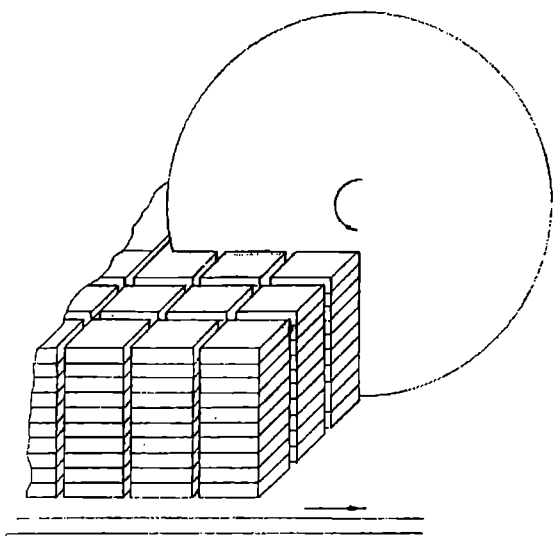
Схема резки групповых заготовок пластинчатых конденсаторов на отдельные заготовки
